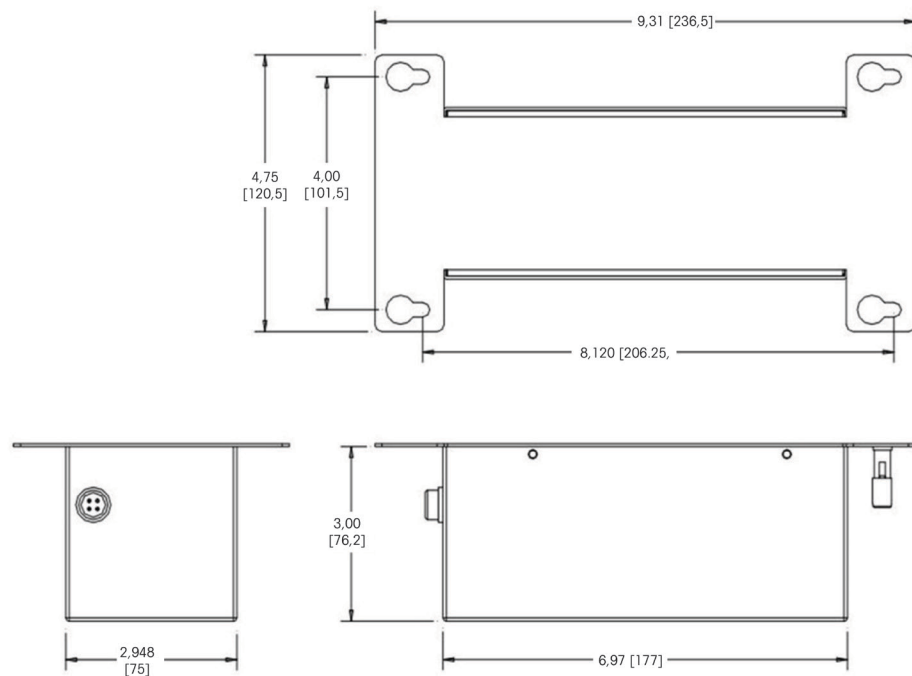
Dimensions générales du bloc de batteries 64060625
